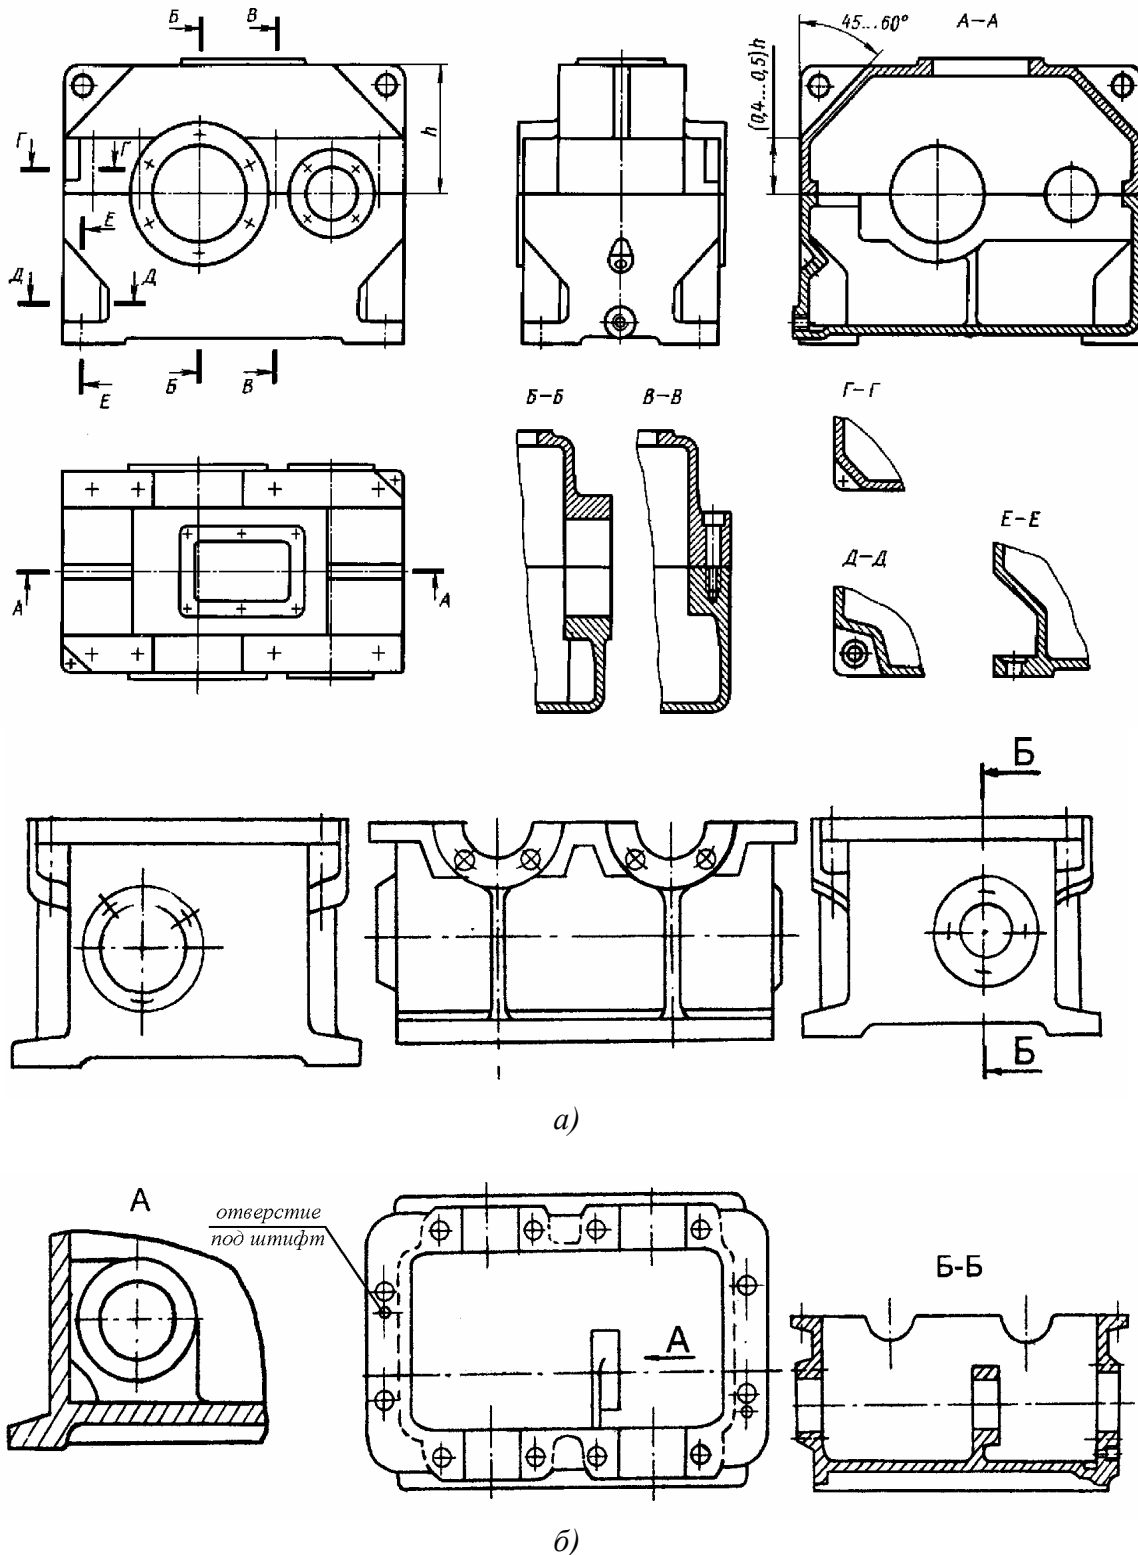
Конструкции разъемных корпусов редукторов: а - современного одноступенчатого цилиндрического; б - червячно-цилиндрического
